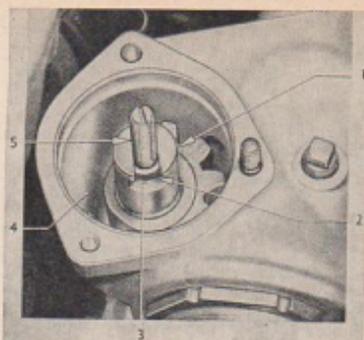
Einstellschraube mit Stehlscheibe in Nut der Lenkstecwelle
